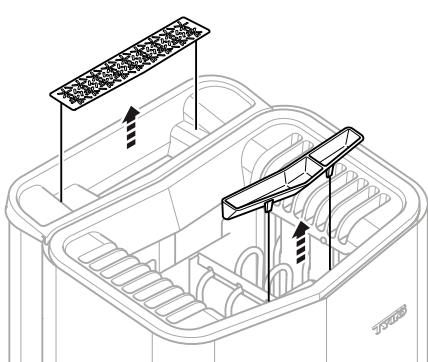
Очистка контейнера для ароматизатора/увлажнителя воздуха и чаши для трав
